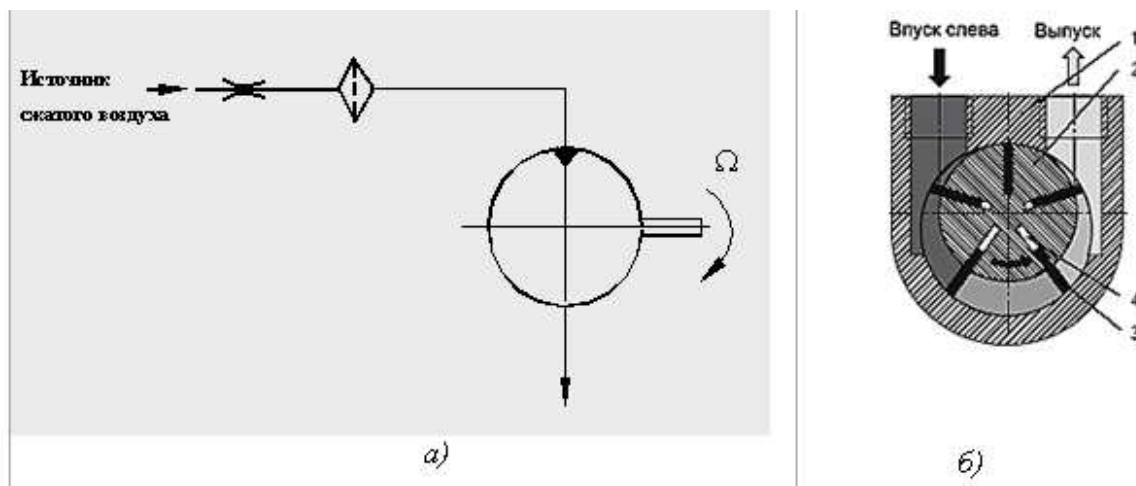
Упрощенная схема силового тракта пневматической вальцовочной машины (а 1- пневмодвигатель; 2- регулируемый дроссель; 3- фильтр) и принципиальная конструкция пневмодвигателя (б- 1-корпус; 2-ротор; 3- лопасти (пластины); 4- пружины).
